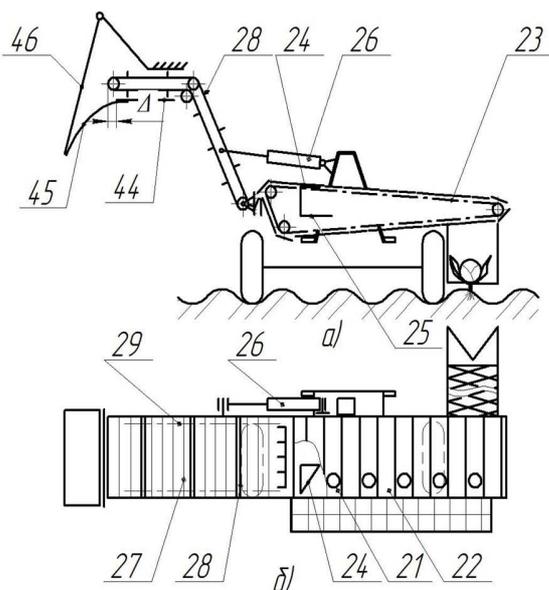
Схема компоновки переборочного транспортер-обрезчика и погрузочного элеватора в капустоуборочном комбайне: а – вид сбоку; б – вид сверху
